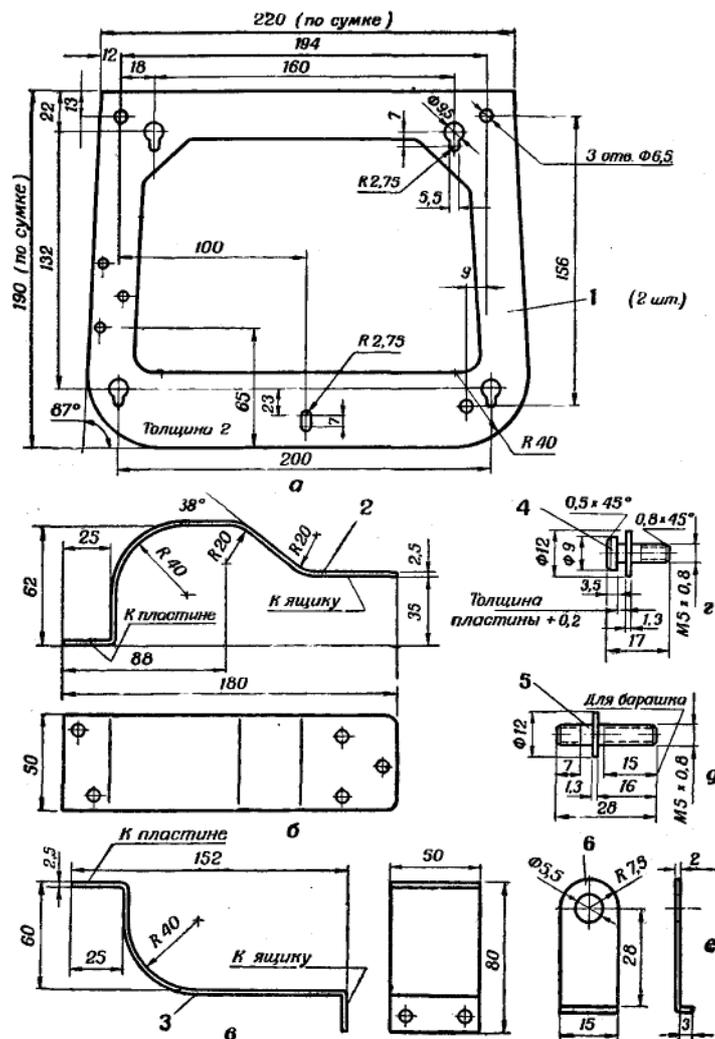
Боковая пластина багажника для установки легкоъемных сумок, правая и левая (а); правый кронштейн крепления пластины к инструментальному ящику (б); левый кронштейн крепления пластины к аккумуляторному ящику (в); грибок (г); шпилька (д); фиксирующая скобка (е)
